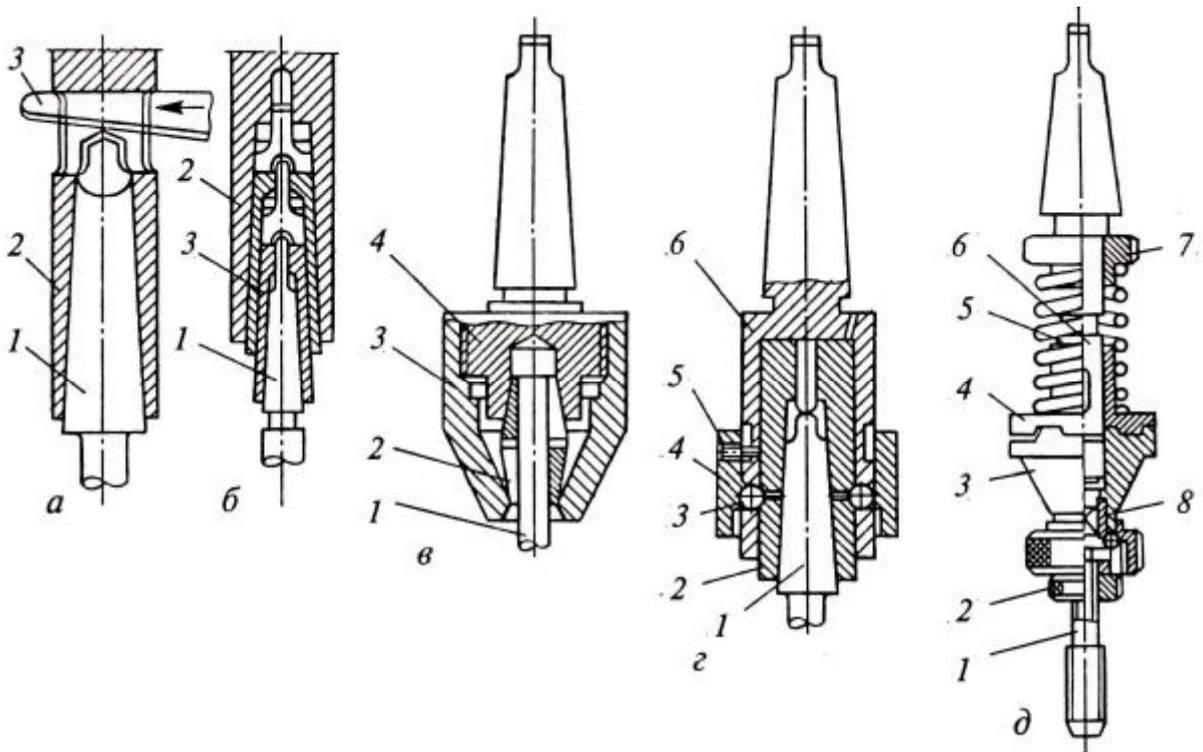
Приспособления для закрепления на сверлильных станках: а, б – инструментов с коническим хвостовиком (1 – инструмент; 2 – шпиндель; 3 – клин); в – инструментов с цилиндрическим хвостовиком (1 – инструмент; 2 – цанга; 3 – гайка; 4 – корпус); з – быстросменный патрон (1 – инструмент; 2 – втулка; 3 – шарики; 4 – кольцо; 5 – винт стопорный; 6 – корпус); д – реверсивный патрон (1 – инструмент; 2 – гайка; 3, 4 – полу-муфты; 5 – пружина; 6 – оправка; 7 – гайка)
